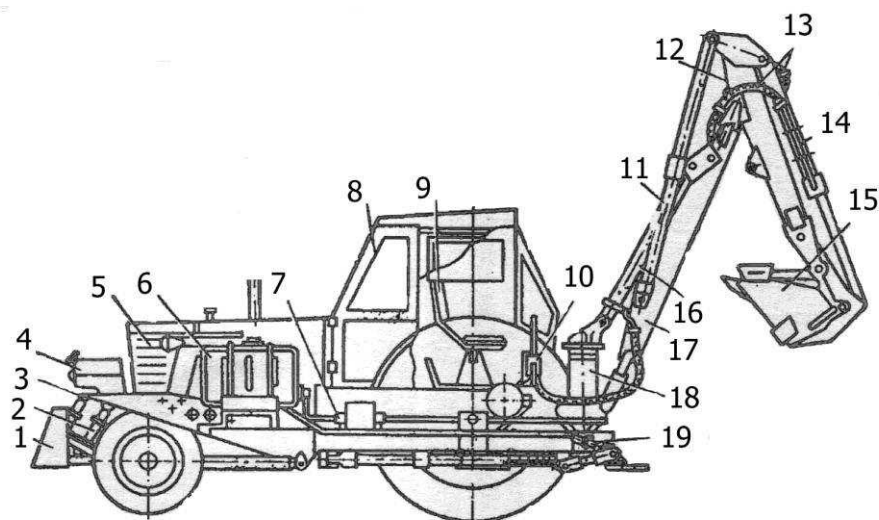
Экскаватор ЭО-2621А: 1 – отвал бульдозера; 2 – гидроцилиндр отвала; 3 – рама навески; 4 – бак; 5 – базовый трактор; 6 – масляный бак с фильтром; 7 – гидронасос; 8 – кабина; 9 – поворотное сиденье; 10 – гидрораспределитель; 11 – гидроцилиндр рукояти; 12 – рукоять; 13 – соединительные трубопроводы; 14 – гидроцилиндр ковша; 15 – ковш; 16 – гидроцилиндр стрелы; 17 – стрела; 18 – поворотная колонка; 19 – гидроцилиндр аутригеров
